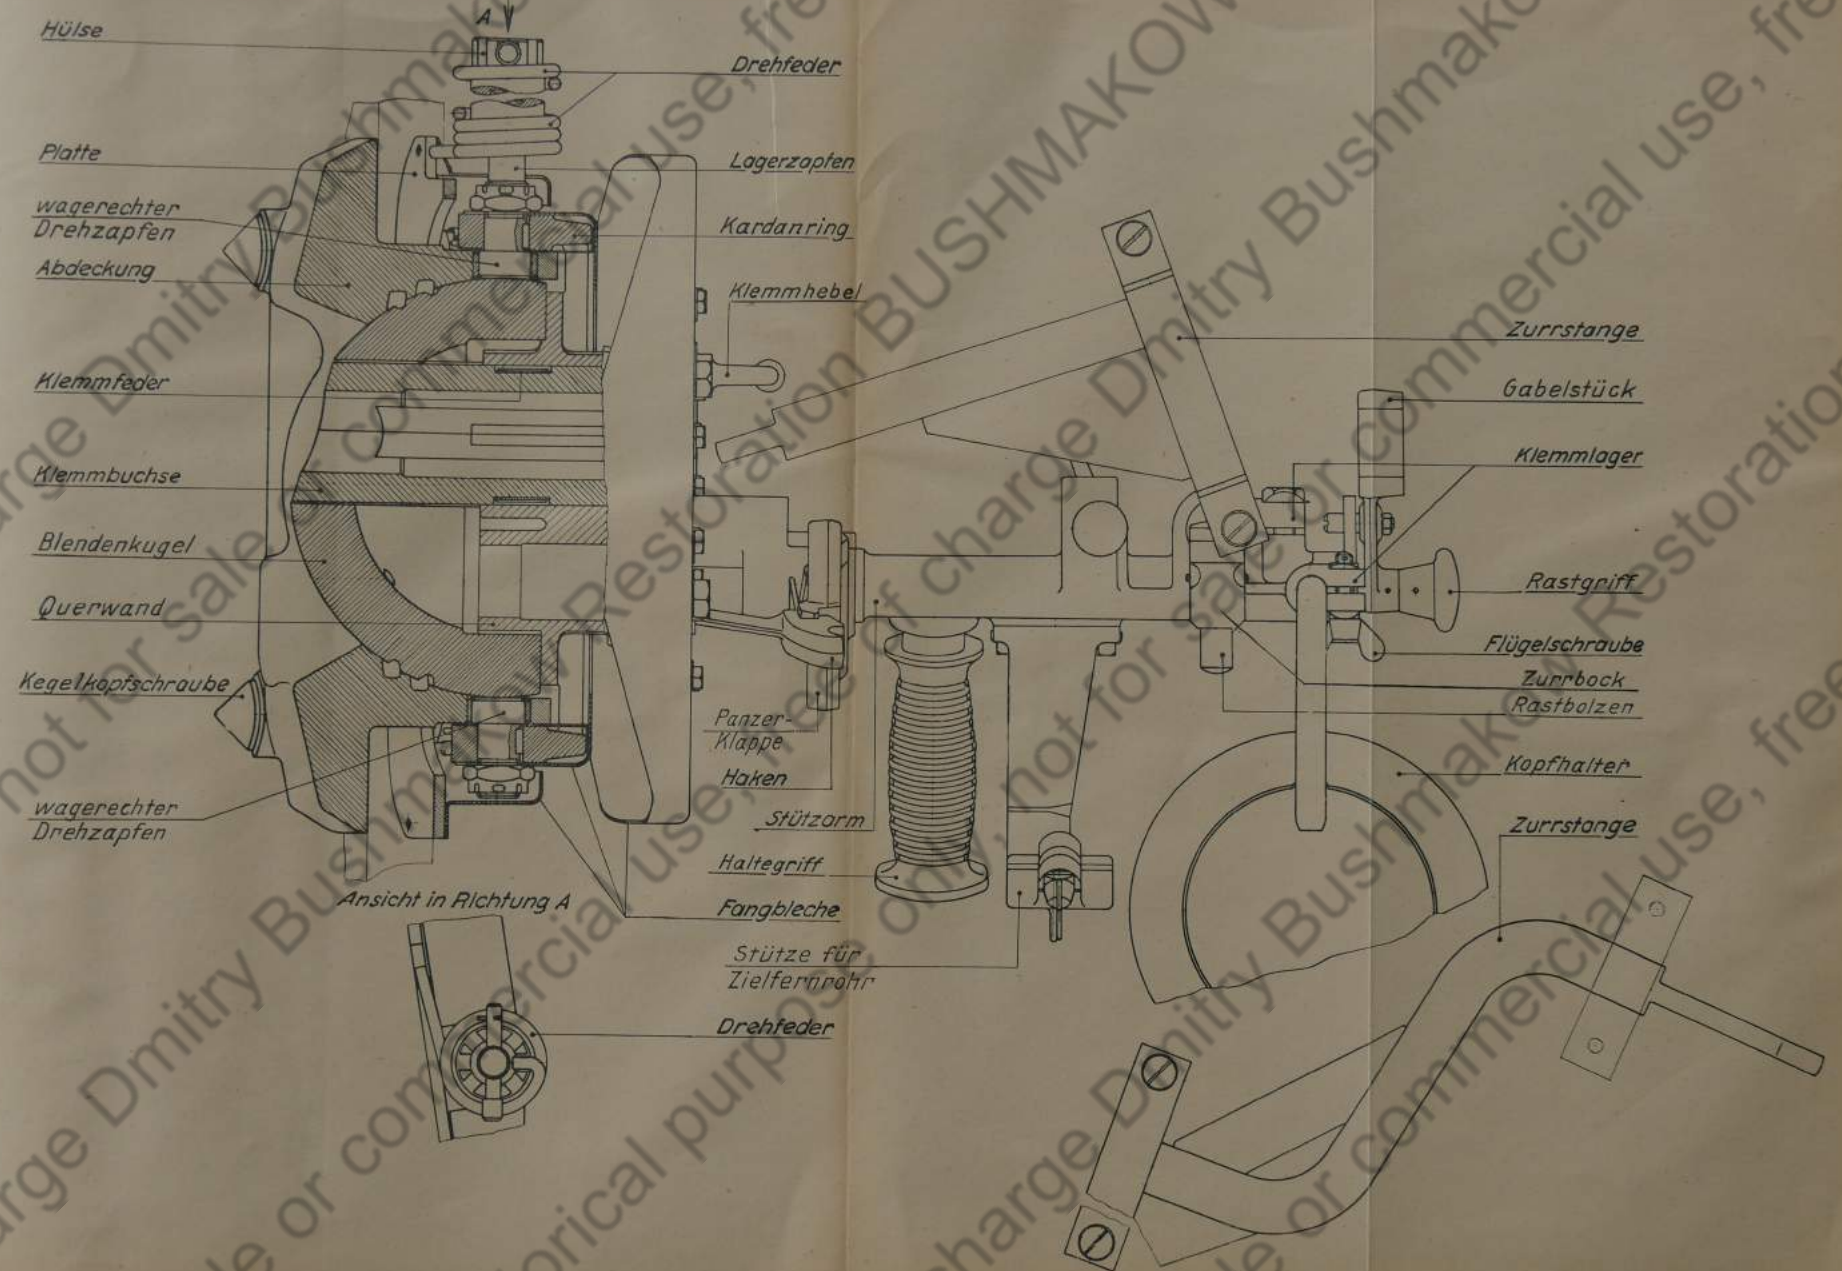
Angelegeblende 30 für MG 34 mit Patronentrommelzuführung, Ausf. D Schnitt und Draufsicht
